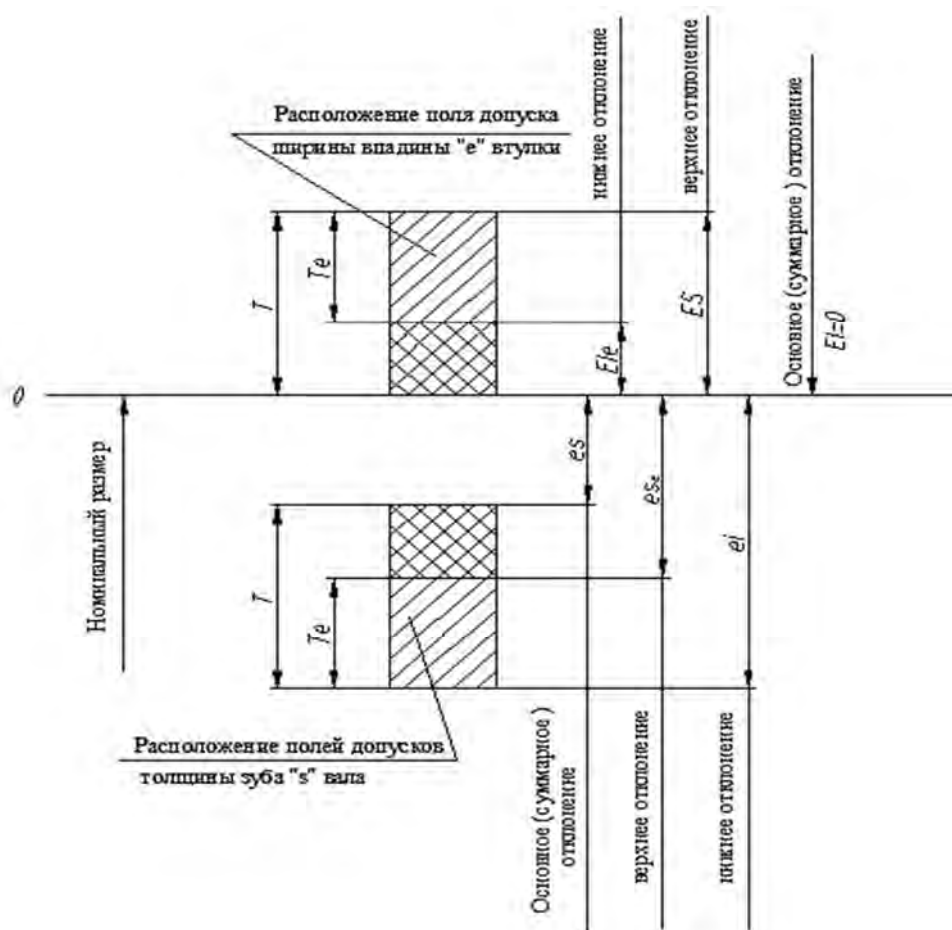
Поля допусков ширины впадин втулки и толщины зубьев вала при центрировании по боковым поверхностям зубьев
